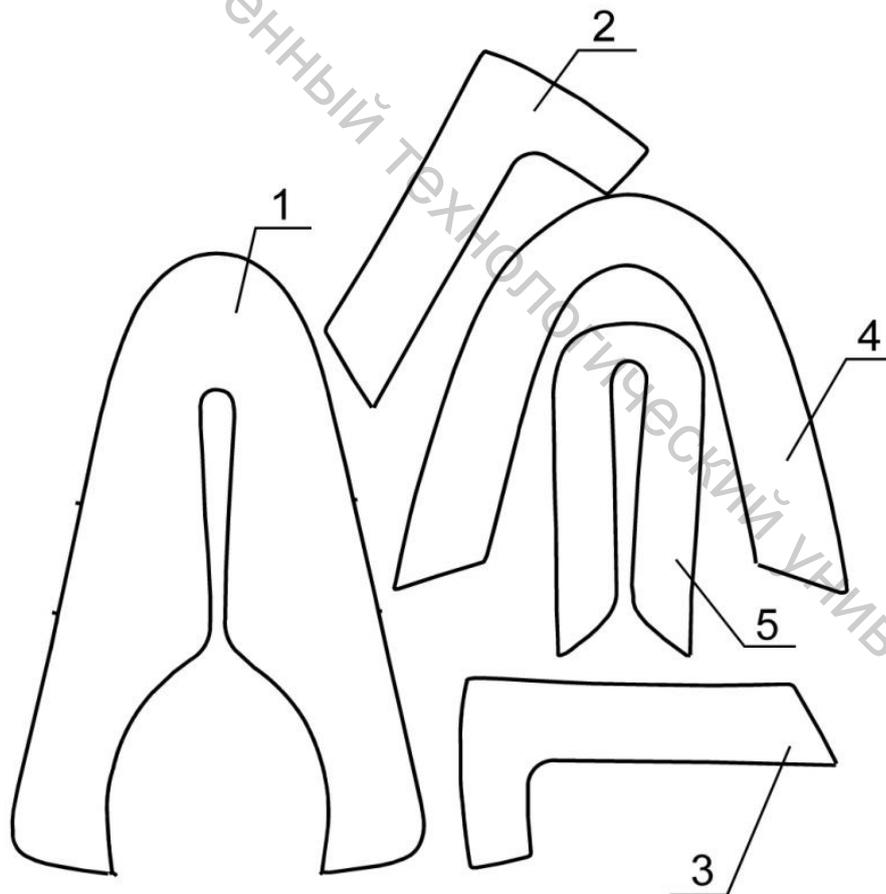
Комплектующие детали плоской заготовки:
